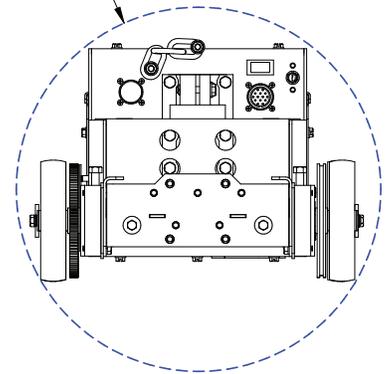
VISTA DE TPO SOLDAGEM DE TUBO
